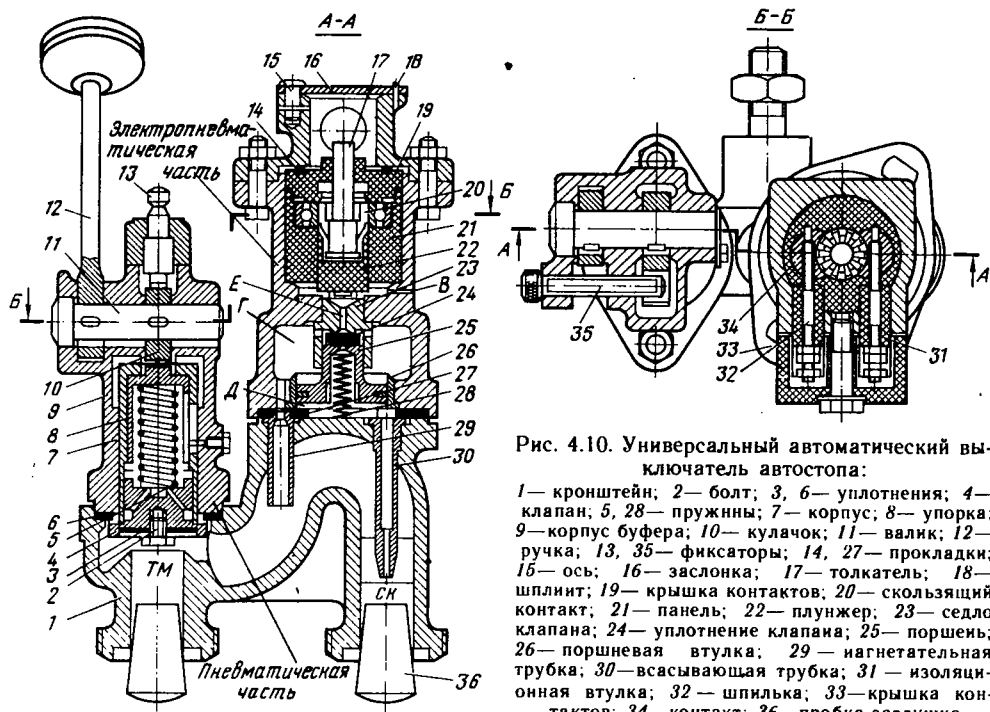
Универсальный автоматический выключатель автостопа:
